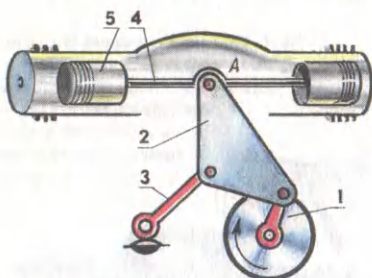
Поршневой двигатель Гускова и Улыбина, оснащенный прямилем Чебышева. Это старинное ползунытое устройство позволяет превратить прямолинейное движение во вращательное. На рисунке обозначены детали двигателя:
